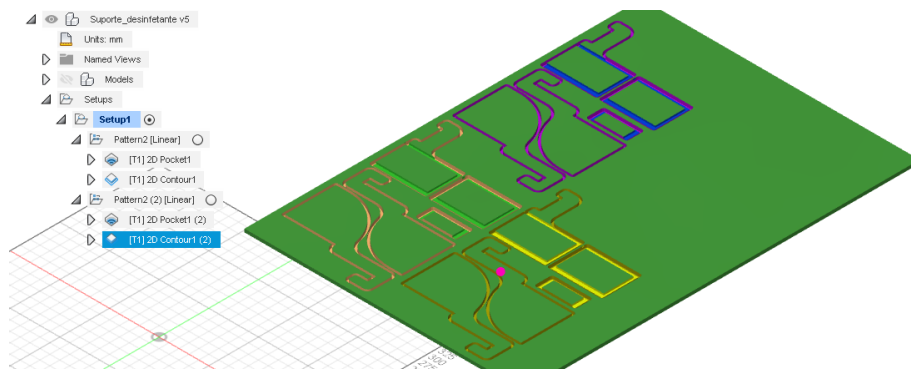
Maquinação para a fresadora CNC do suporte do desinfetante e pano
